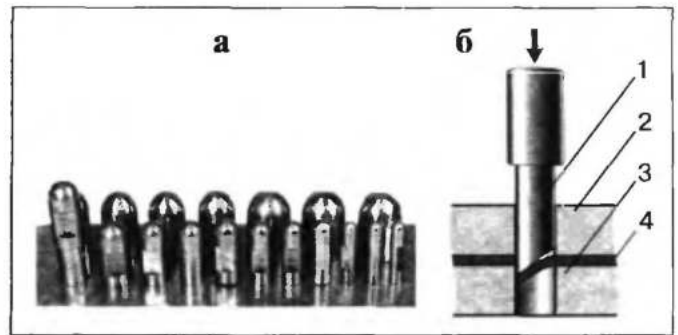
Пробойники для отверстий в прокладках: а — общий вид комплекта; б — схема работы: 1 — пробойник; 2 — крышка; 3 — основание; 4 — прокладка
